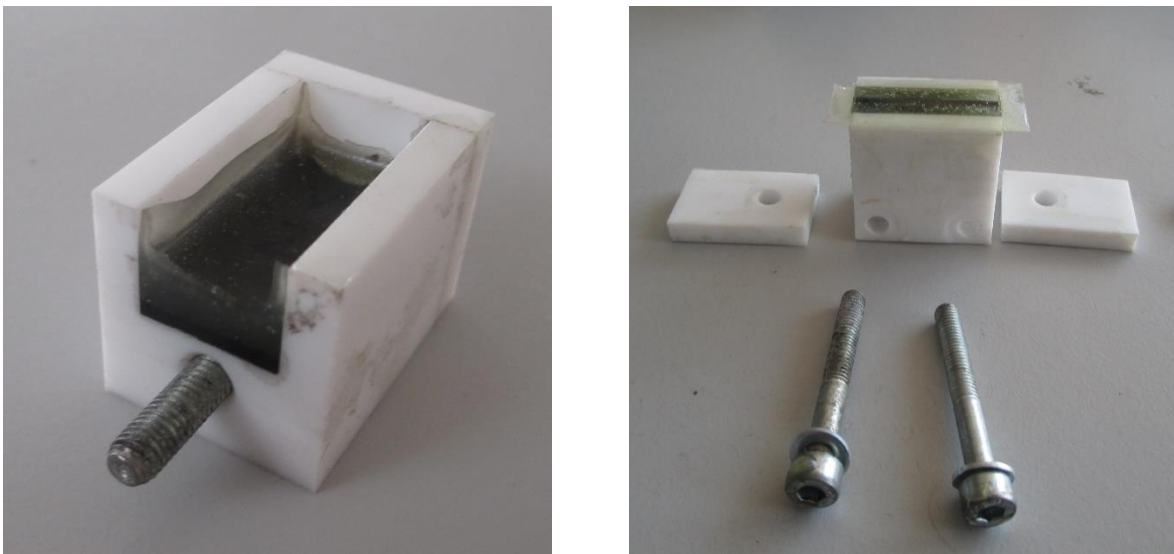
Moldes em PTFE para fabrico dos provetes híbridos de Araldite: Molde I (à esquerda) e Molde III (à direita).
